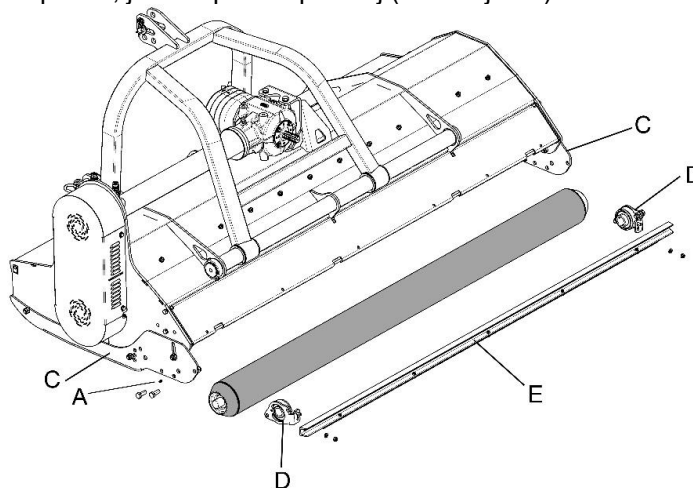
Pozycja zewnętrzna rolki wspierającej
